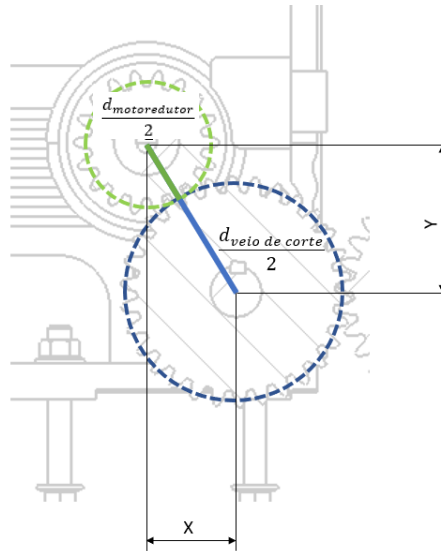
Esboço das distâncias a calcular para dimensionamento da roda dentada do veio do moto redutor
